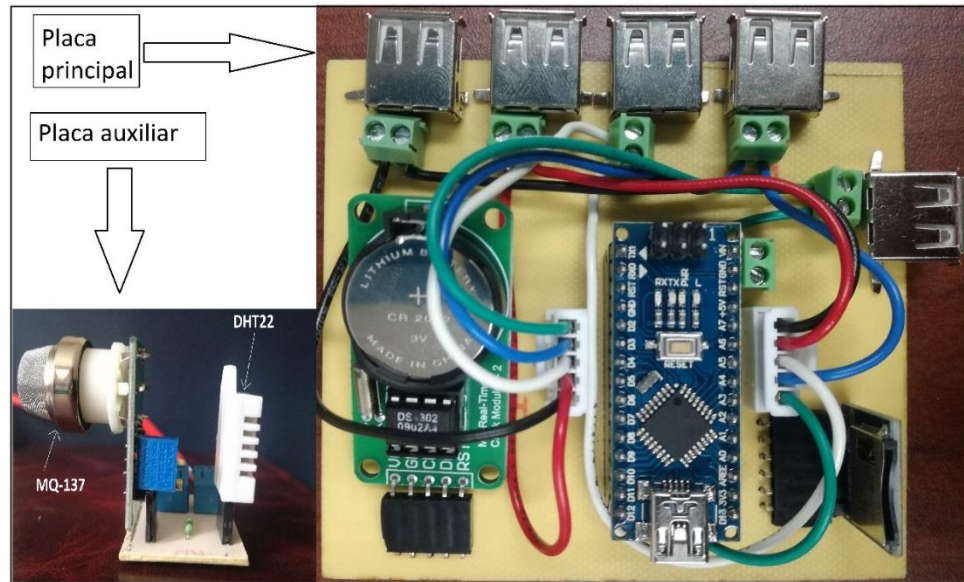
Placas de circuito impreso con los componentes soldados, basados en los diseños de los circuitos desarrollados, 3 placas principales y 15 auxiliares.
